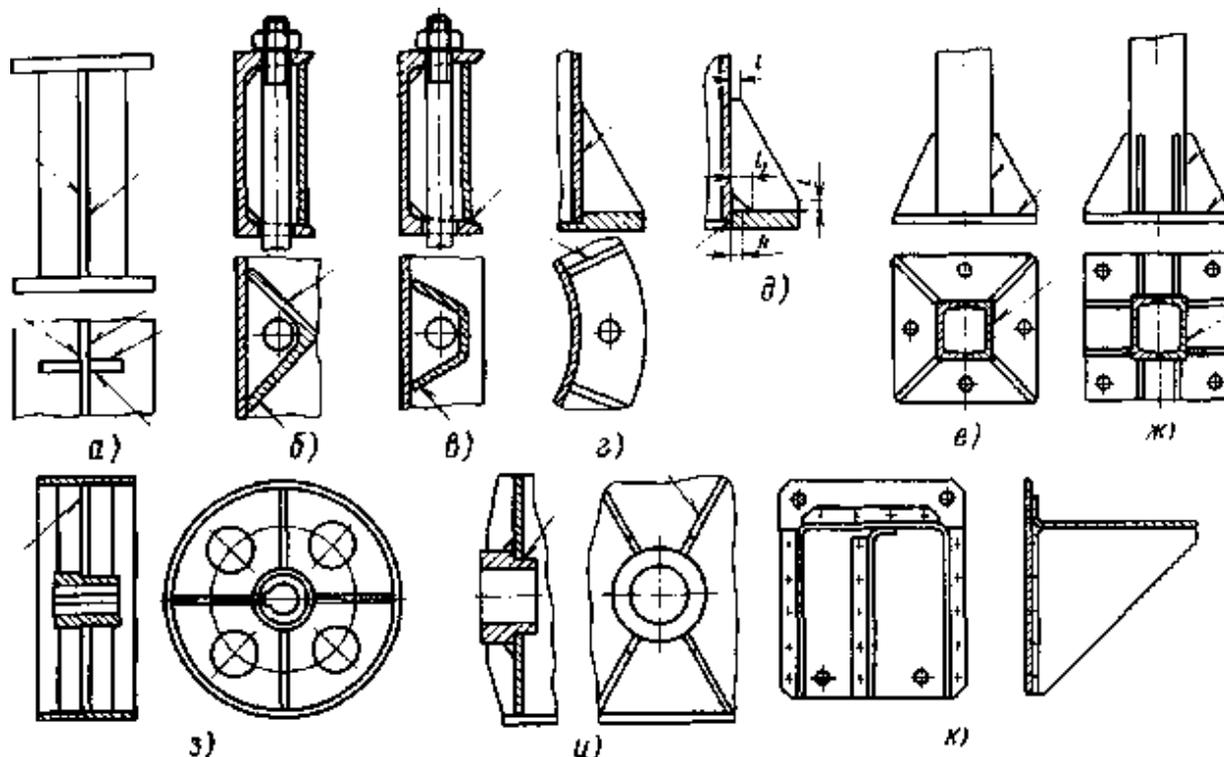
Примеры использования ребер в сварных конструкциях
